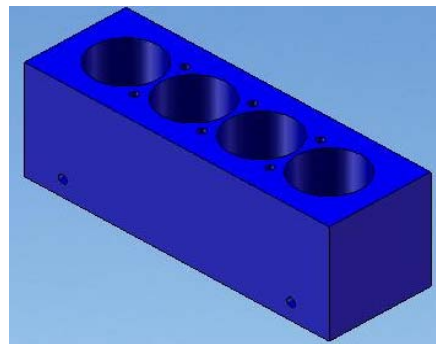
Alt İtici Mili Ve Dip Şekillendirme
